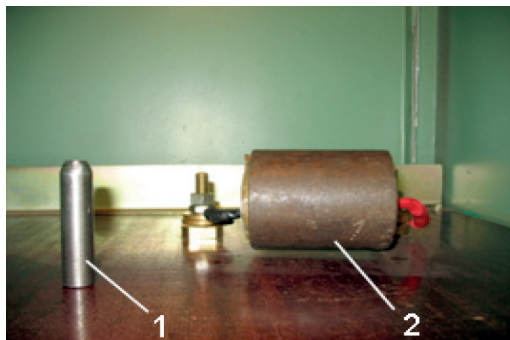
Индуктор цилиндрический, установленный на рабочий стол МИУ: 1 — упрочняемая деталь; 2 — цилиндрический индуктор
